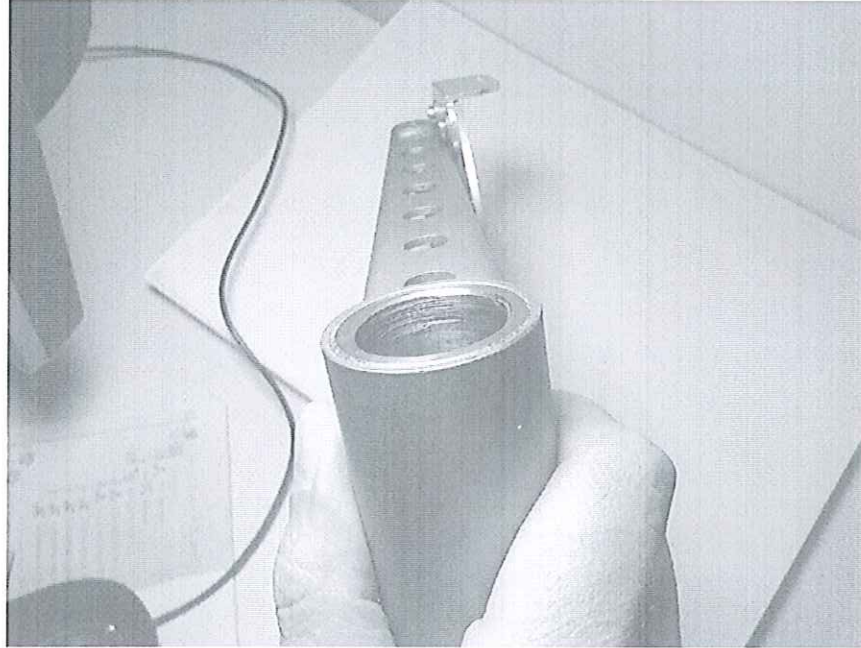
Beschädigtes Teil / *damaged part
